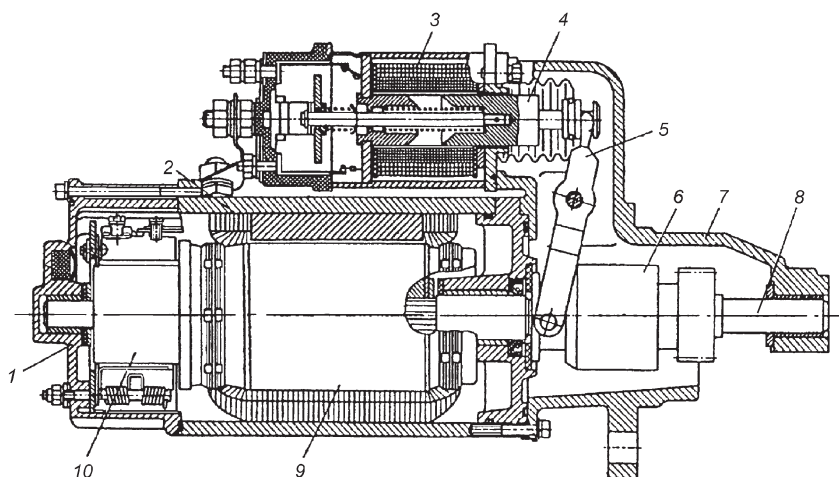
Конструкция стартера со встроенным цилиндрическим редуктором с внешним зацеплением:
